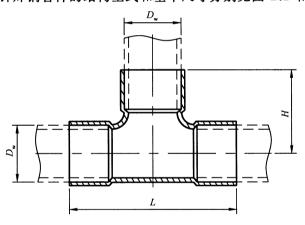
等径三通 ST 承插式钎焊铜管件
